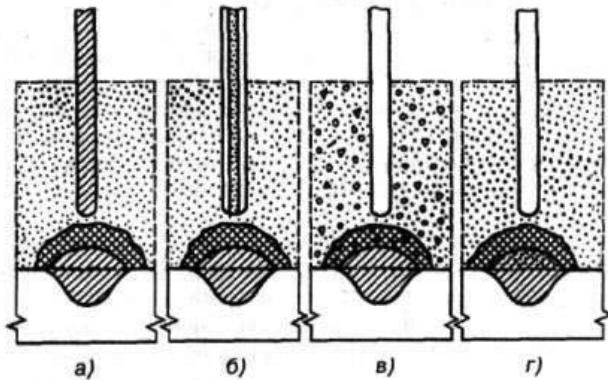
Способи легування наплавленого металу: а – використання зварювального дроту; б – порошкового дроту; в – через керамічний флюс; г – шлікерне покриття
